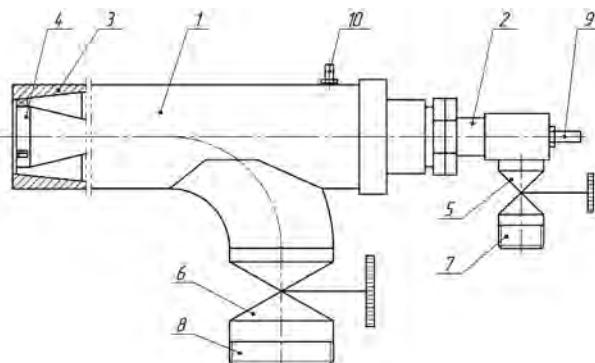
Общий вид горелки: 1 – корпус; 2 – газовая труба; 3 – газо-воздушный насадок; 4 – стабилизатор горения; 5 – регулятор расхода газа; 6 – регулятор расхода воздуха; 7, 8 – ниппель для присоединения гибкого шланга; 9, 10 – ниппель для присоединения переносного (стационарного) напоромера для измерения давления соответственно газа и воздуха.
